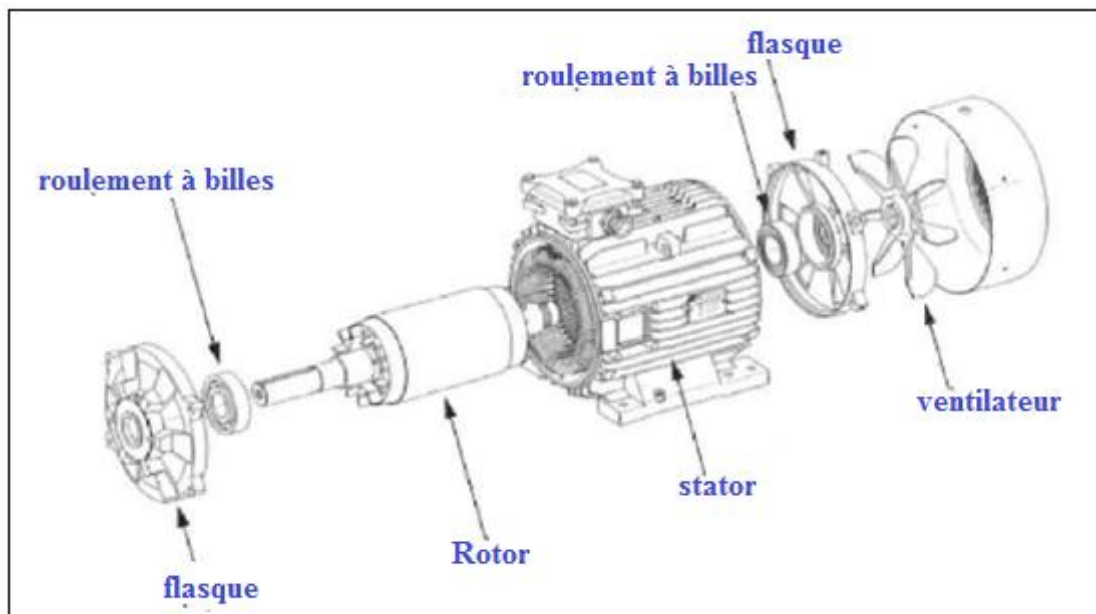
Structure d'une machine asynchrone à cage d'écureuil ou à rotor massif [1].
